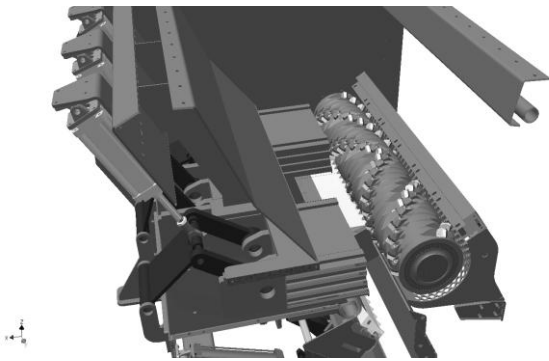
3D-Ansicht der Seriemaschine mit geteilter Zuführung und Grobteilaustrag
